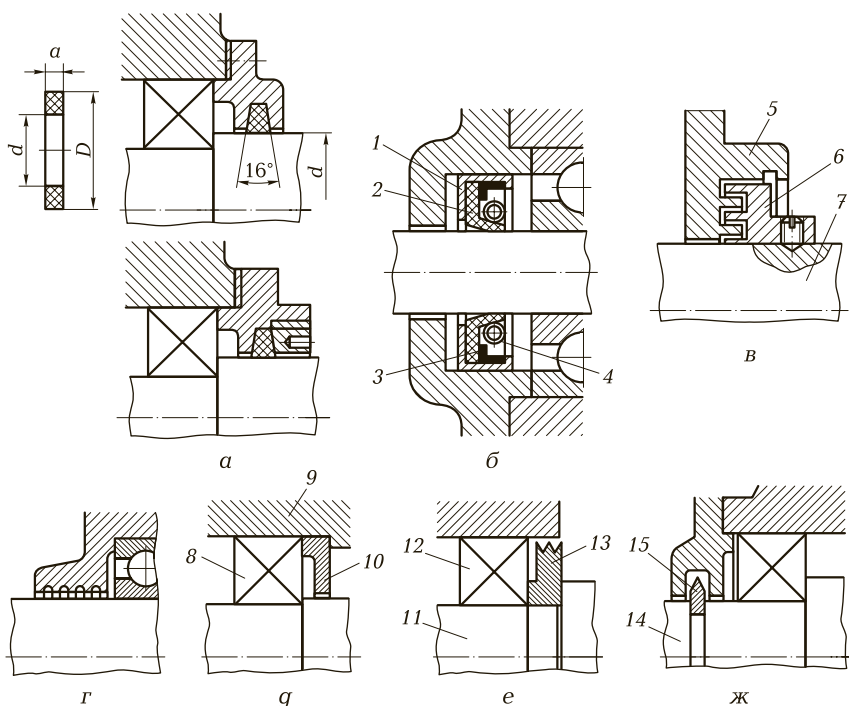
Уплотнение подшипниковых узлов с подшипниками качения:
